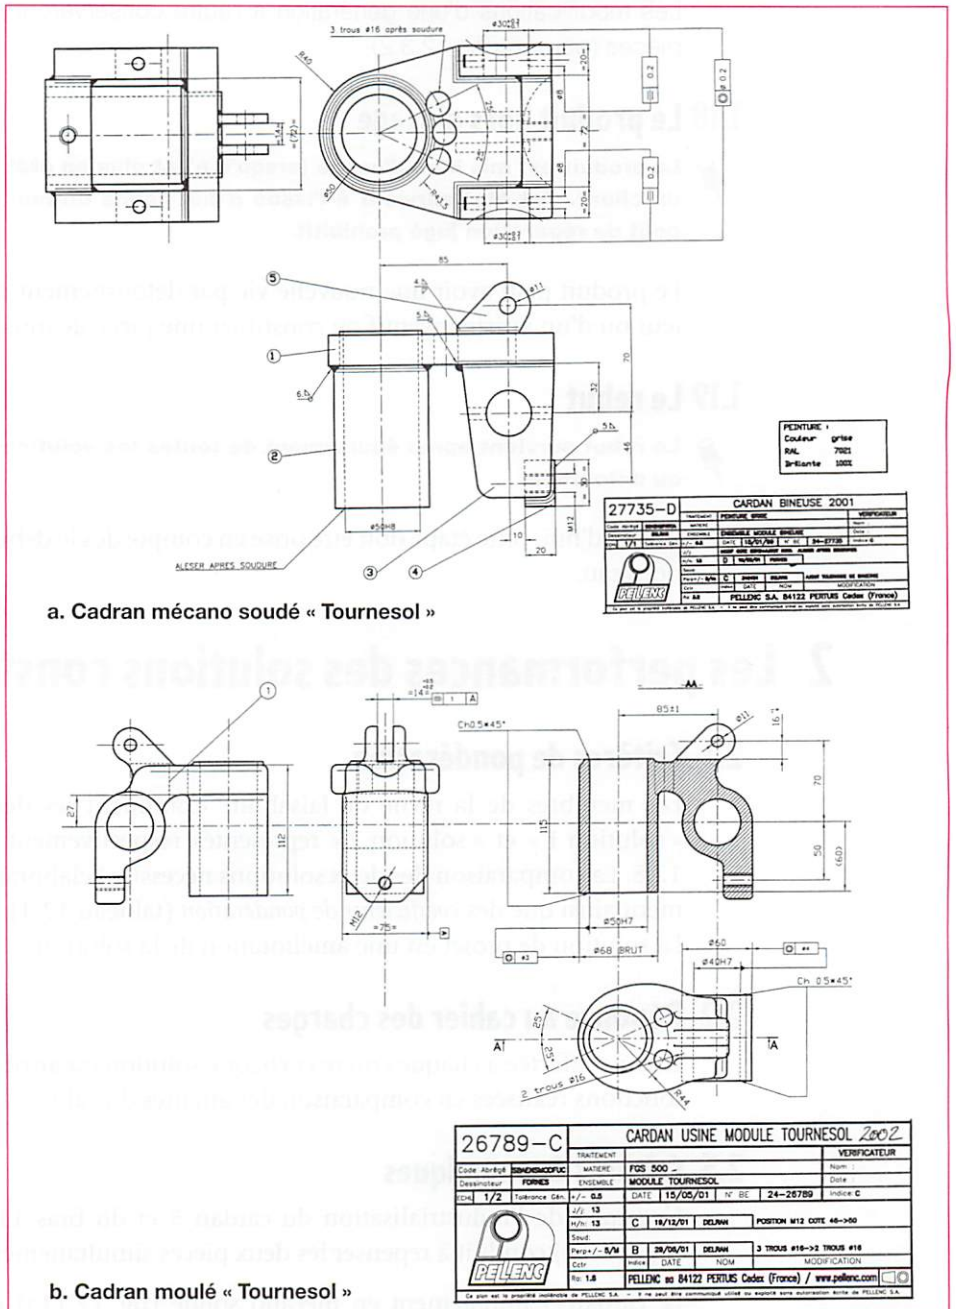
Cardan mécano soudé et cadran moulé « Tournesol »
